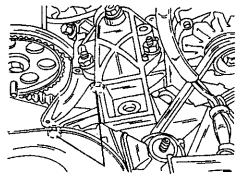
Отвернуть только два указанных болта опоры двигателя.
